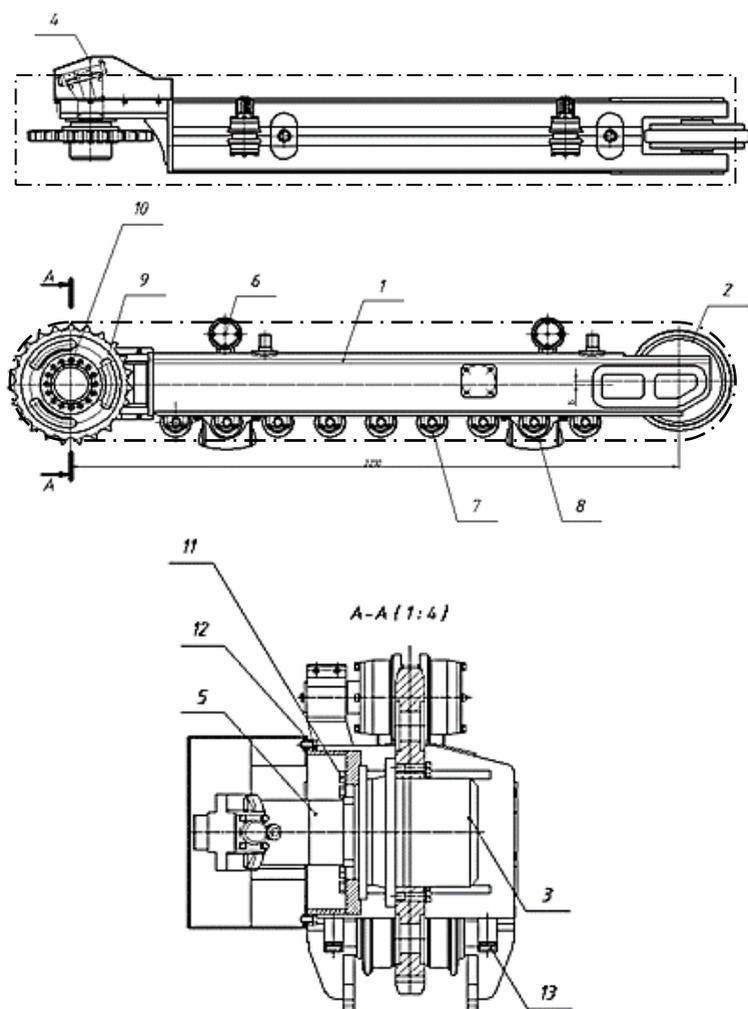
Тележка гусеничная: 1 – лонжерон; 2 – механизм натяжения гусеницы; 3 – редуктор привода хода; 4 – кожух гидромотора; 5 – гидромотор привода хода; 6 – ролики поддерживающие; 7 – катки опорные; 8 – ограничители; 9 – ведущая звездочка; 10, 11, 12, 13 – болты
